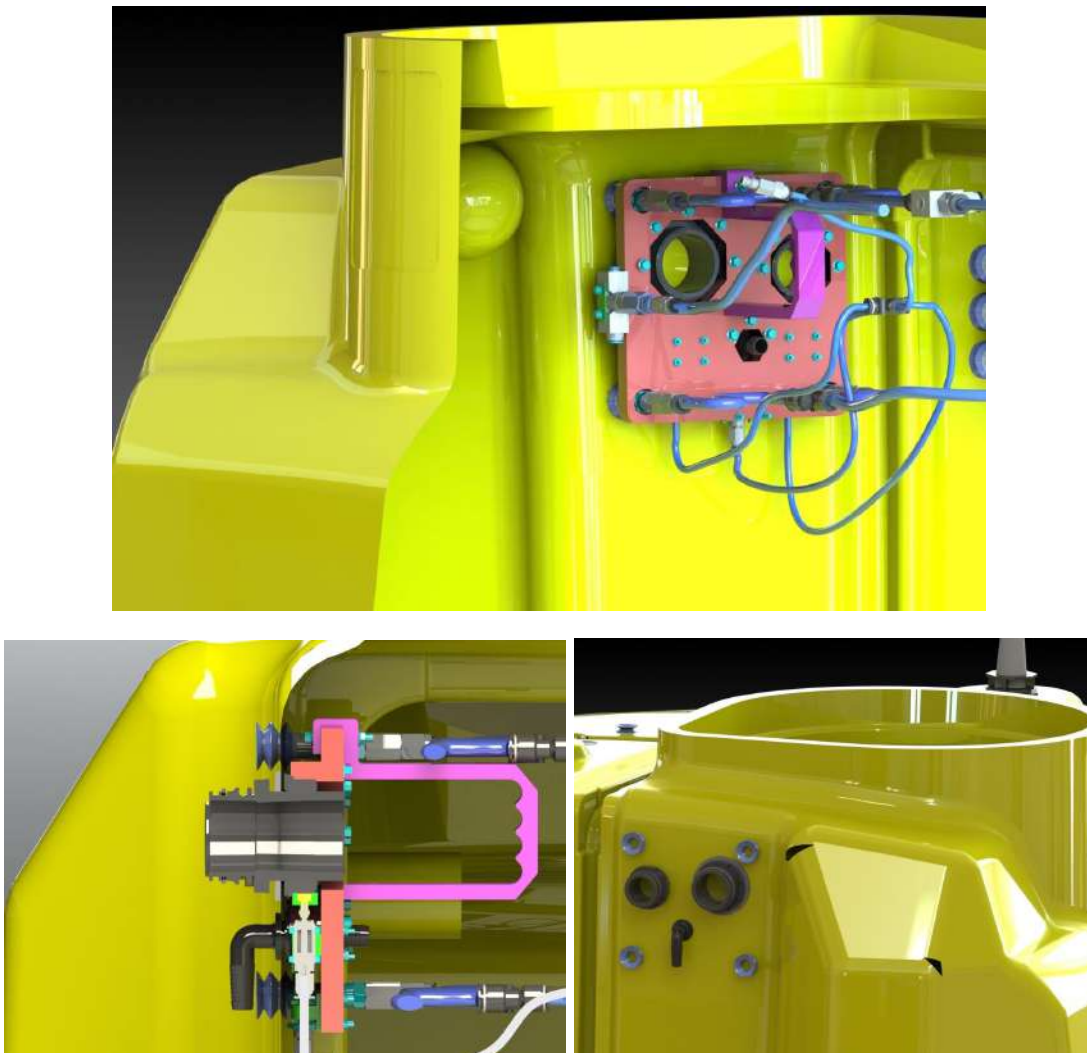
Cabezal para Carga Tanque - Retorno a Tanque - Desagote colocado en posición de montaje.
